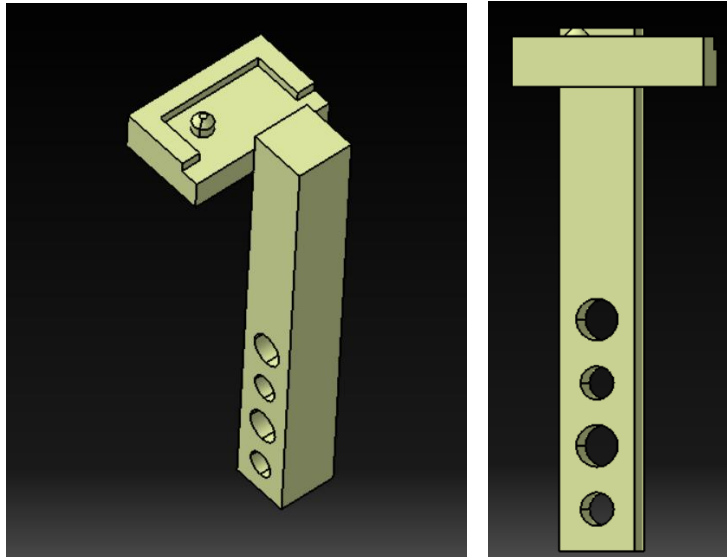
TORRE DE SOLDADURA #2
